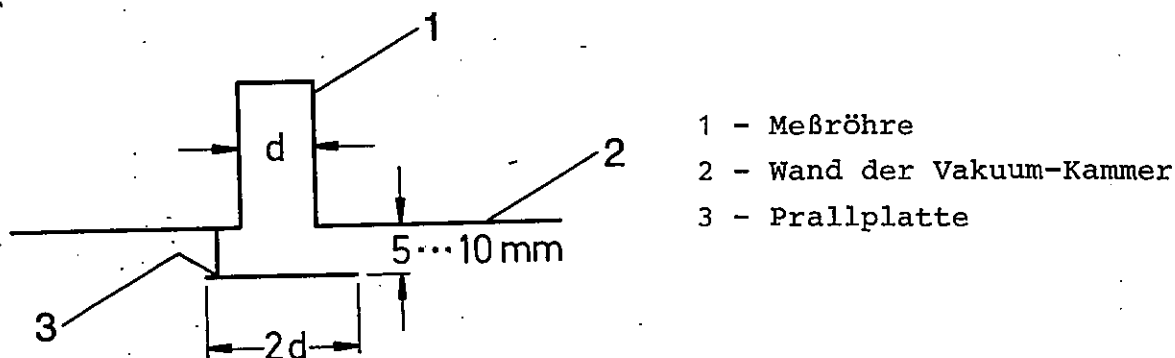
Lage inner Prallplatte am Eingang einer Vakuum-Meßröhre
